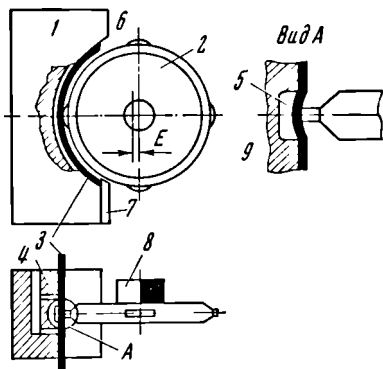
Расположение видеоголовок в диске и диска в направляющей камере. 1 — направляющая камера; 2 — диск с видеоголовками; 3 — лента; 4 — щели вакуумного присоса; 5 — канавка; 6 — скос на камере; 7 — упор для ленты; 8 — obturator фотодатчика; 9 — видеоголовка, E — смещение центра кривизны направляющей камеры от центра вращения диска; А — контакт головки с лентой
